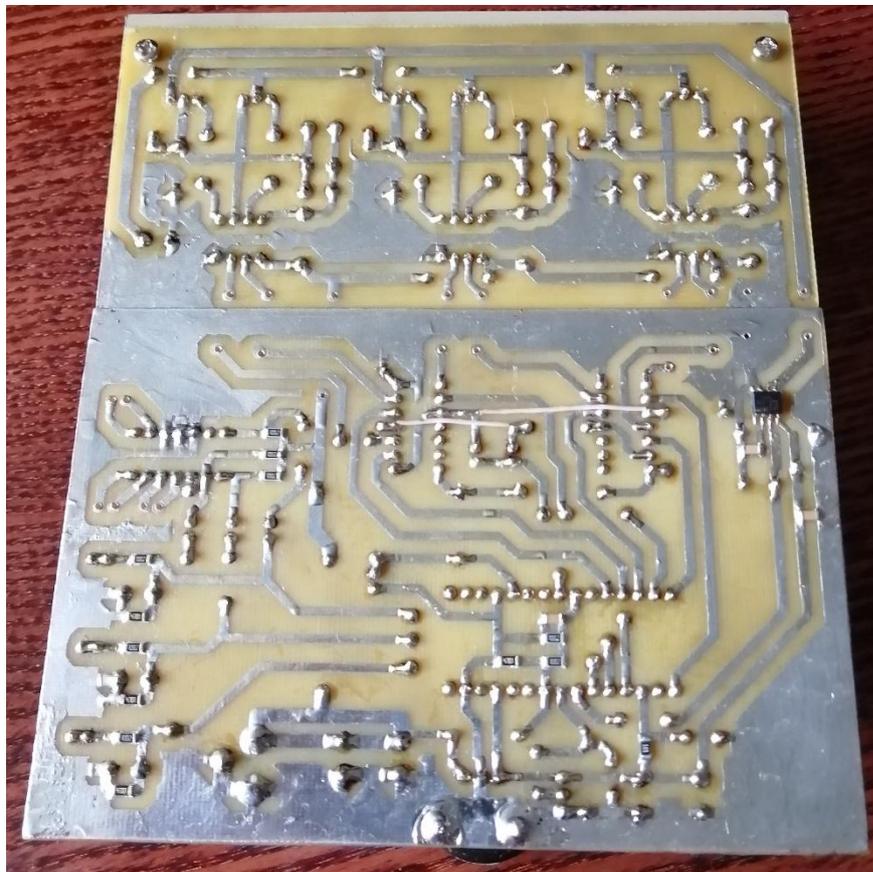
Внешний вид печатных плат изделия (вид со стороны проводников)
